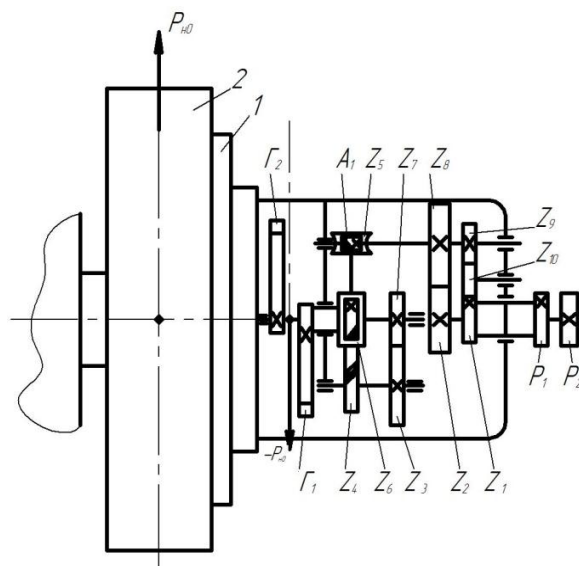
Балансирующее устройство шлифовального станка с ручным приводом
